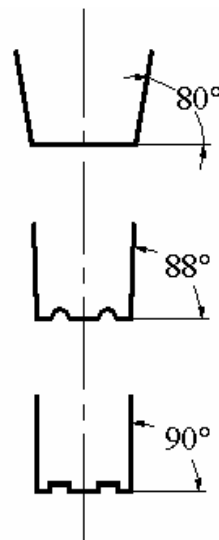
Схема формовки гофр на швеллерном профиле
